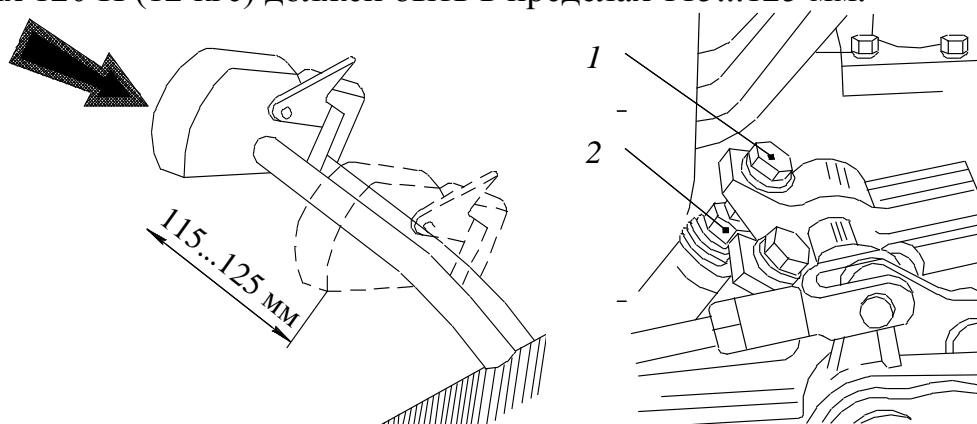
Схема проверки и регулировки рабочих тормозов:
